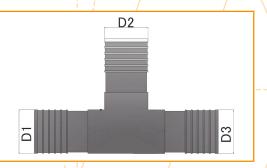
Пресс-тройник Тип 1 типоразмера 50 и более
